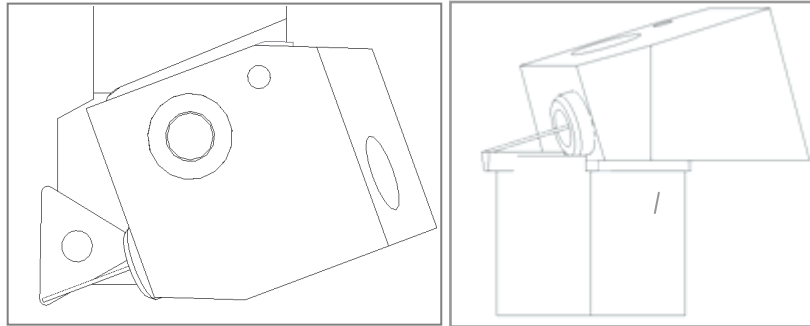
Point d'impact 1 : sur la face de coupe (Ay).
